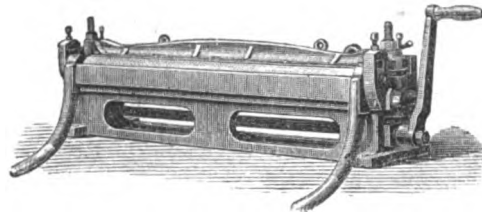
Universal-Abkante-, Falz- und Umschlagmaschine.
